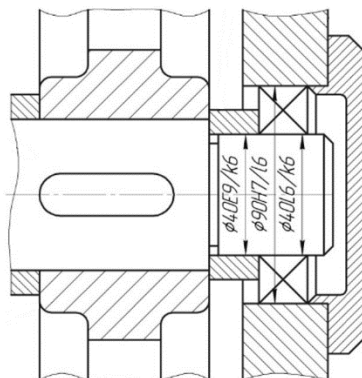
Обозначение посадок подшипников качения на сборочных чертежах
